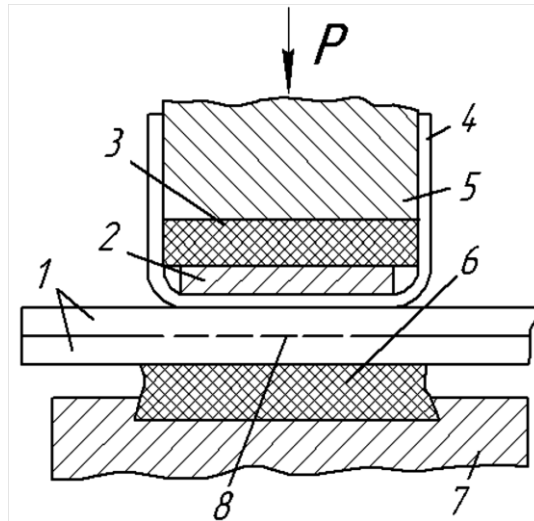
Термоімпульсне зварювання: 1 – зварювані плівки; 2 – нагрівальний інструмент; 3 – теплоелектроізоляційна прокладка; 4 – антиадгезійна прокладка; 5 – рухома частина зварювального пристрою; 6 – антиадгезійна підкладка; 7 – нерухома частина зварювального пристрою; 8 – зварний шов.
